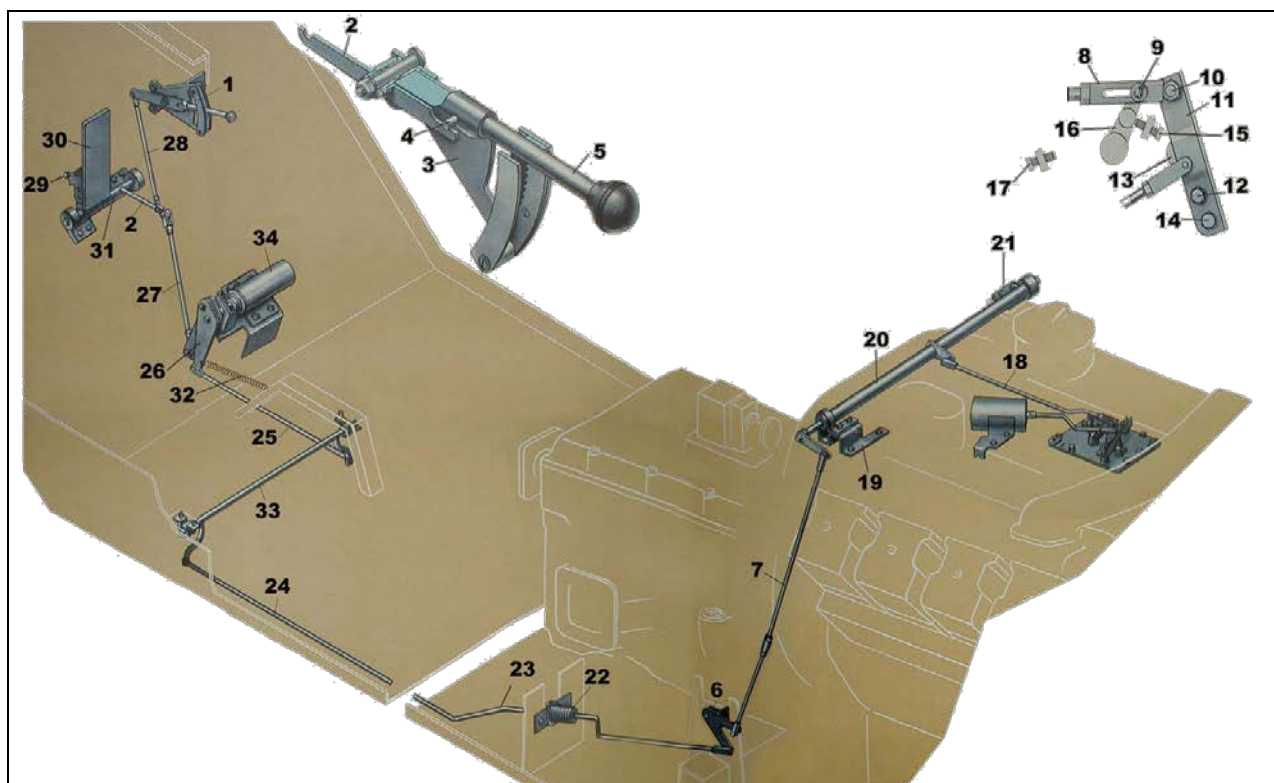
ОК-9 – Органы управления БТР-80 и привода подачи топлива и остановки двигателя
